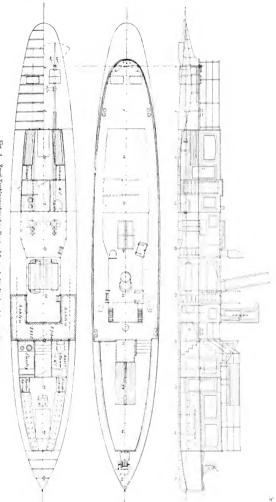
Zwei-Turbinenschrauben-Boot. Längsschnitt, Deckansicht und Staumgsplan.
